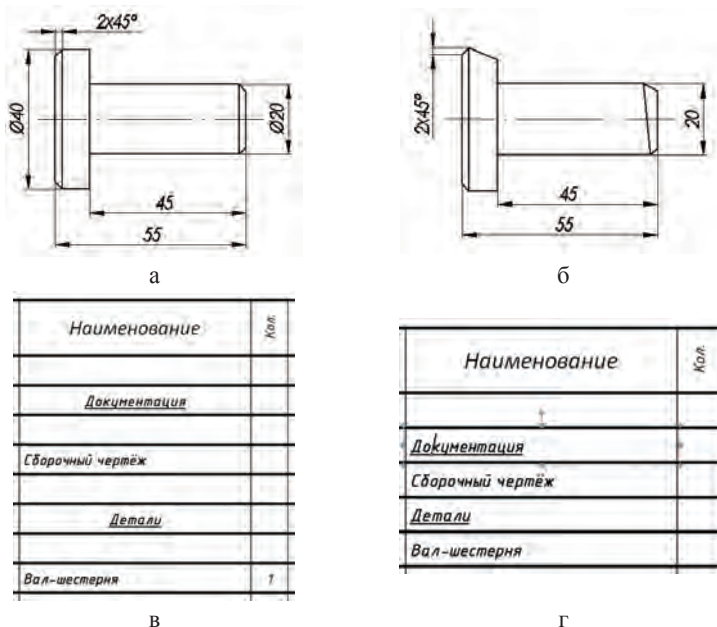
Ошибки при выполнении чертежей и подготовке КД
